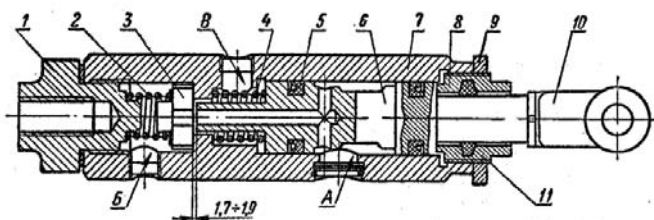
Следящее устройство: 1 — переходная гайка; 2, 4 — пружина; 3 — клапан; 5 — манжета; 6 — плунжер; 7 — корпус; 8 — регулировочная гайка; 9 — контргайка; 10 — вилка; 11 — войлочное кольцо, А — отверстие, соединенное с атмосферой; Б — отверстие, соединенное с пневмосистемой; В — отверстие, соединенное с пневмокамерой
